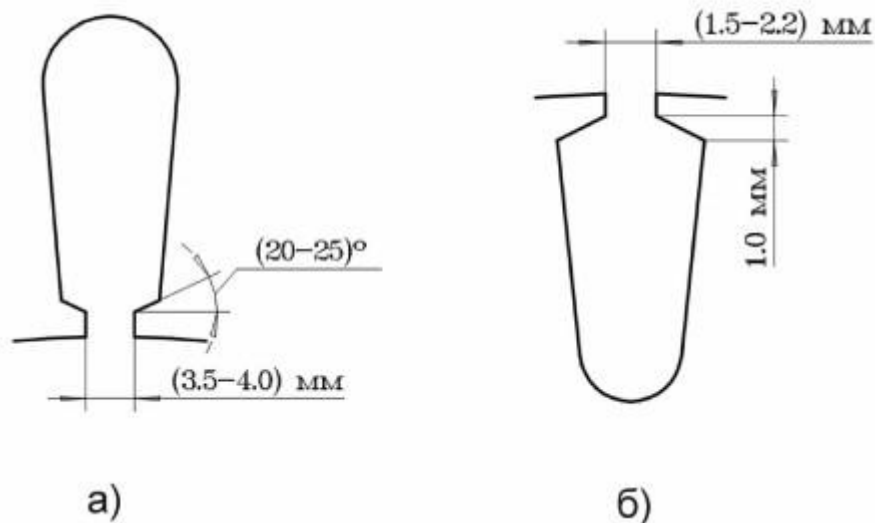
Пазова геометрія: а) паз статора; б) Паз ротора
